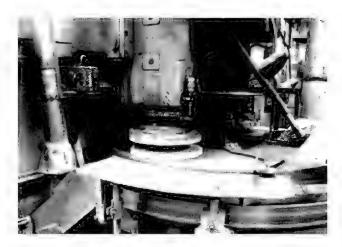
Общий вид плоскообдирочного станка модели KIII-64
